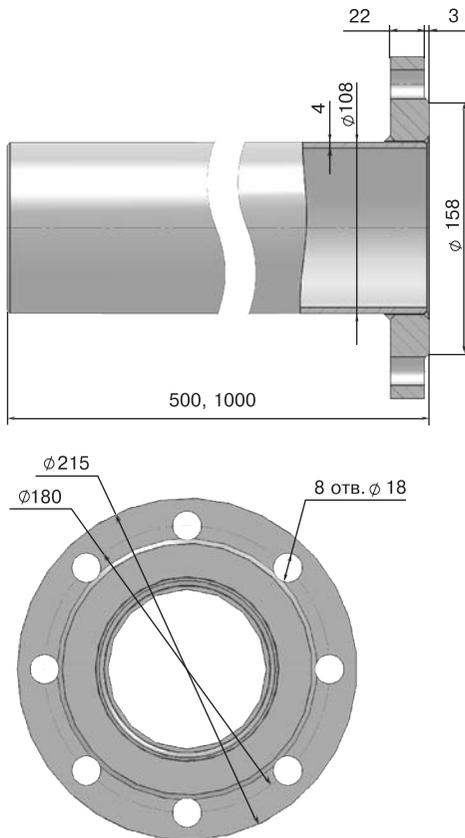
Габаритные и установочные размеры КМЧ 3 для КАРАТ-РС-100
